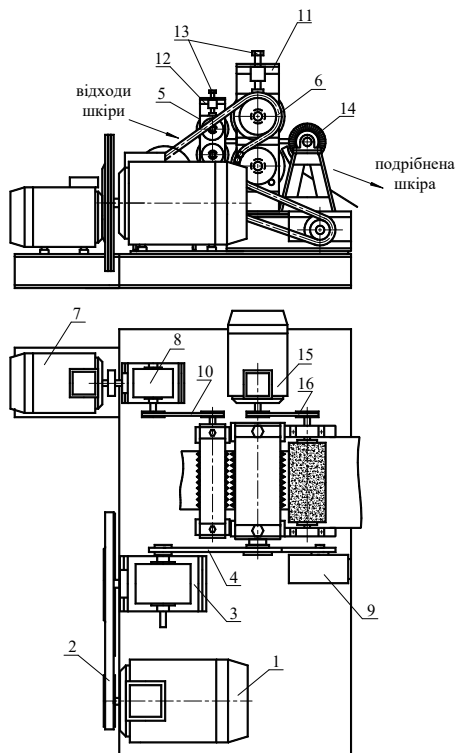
Схема технологічного валкового пристрою для розволокнення натуральних шкір: 1, 7, 15 – електродвигуни; 2 – пасова передача; 3, 8 – черв'ячний редуктор; 4, 10, 16 – ланцюгова передача; 5, 6 – валкові пристрої; 11, 12 – стійки; 13 – упорні болти; 14 – голкофреза
